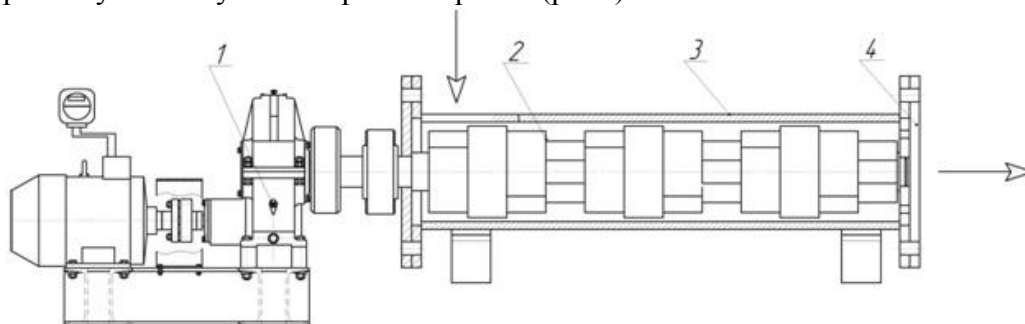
Експериментальна установка: 1 - привід; 2 - кулачковий робочий орган; 3 - двовальний корпус; 4 - решітка для вивантаження тіста
